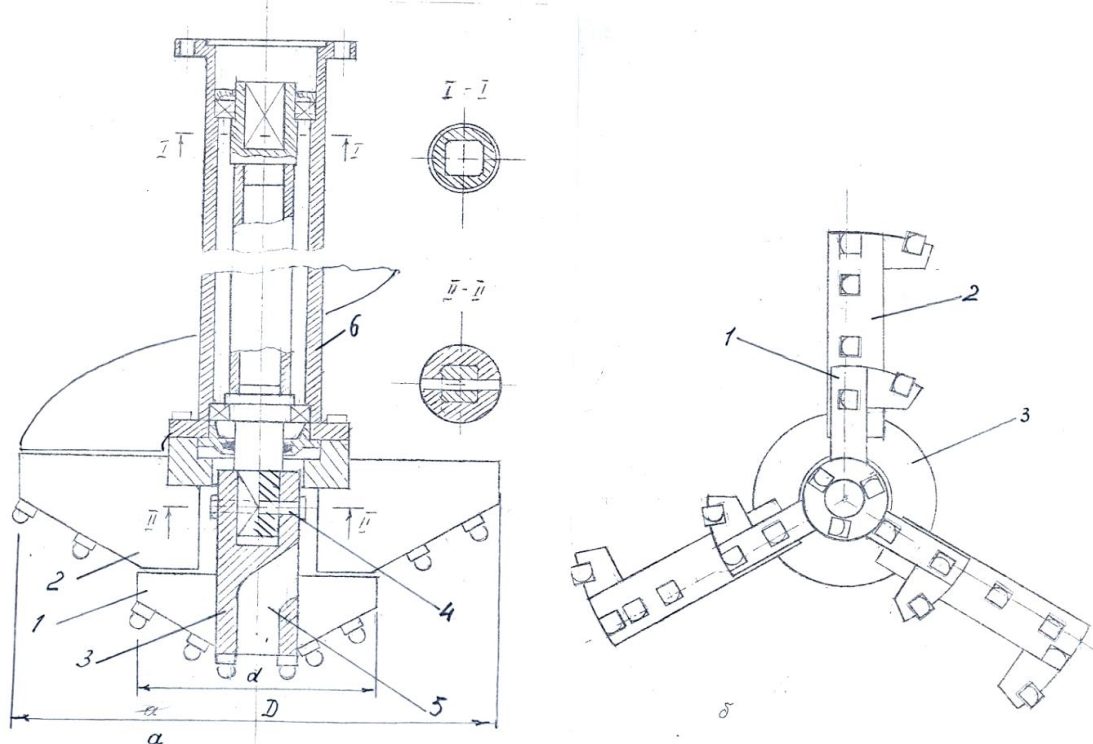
Конструктивна схема бурильного обладнання з роздільним обертанням; а – бур зі штангою; б – схема розстановки різців.
